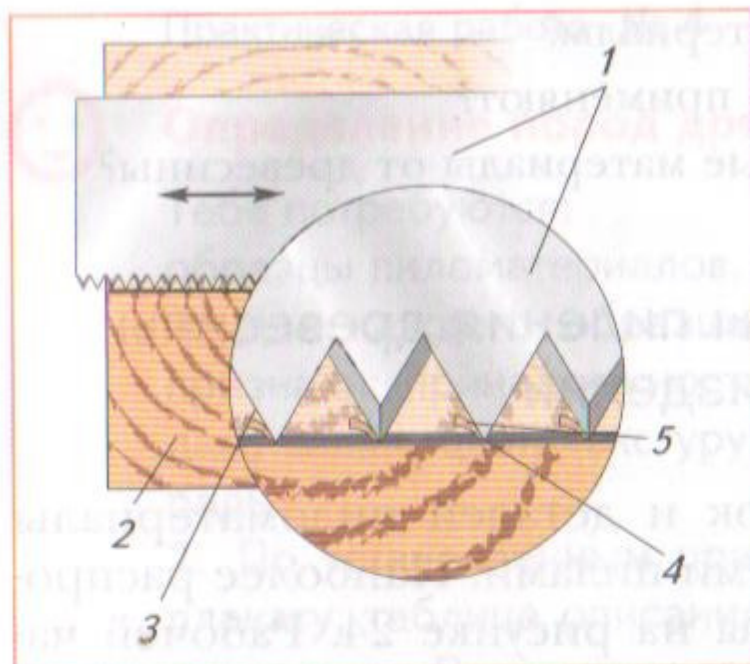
Поперечное пиление древесины: 1 — пила; 2 — заготовка; 3 — режущая кромка зуба; 4 — вершина зуба; 5 — опилки
